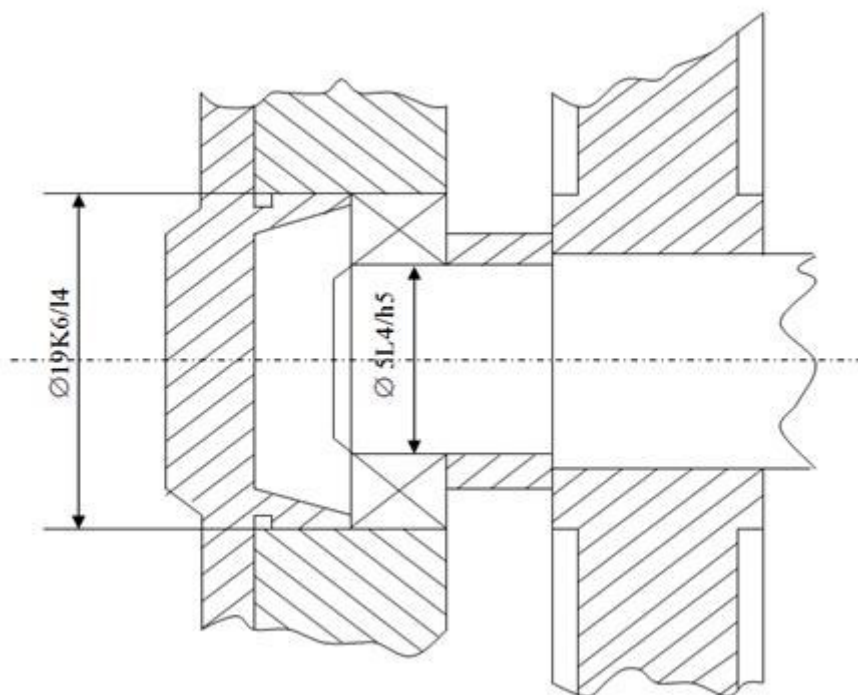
Эскиз сопряжения подшипника с валом и корпусом
